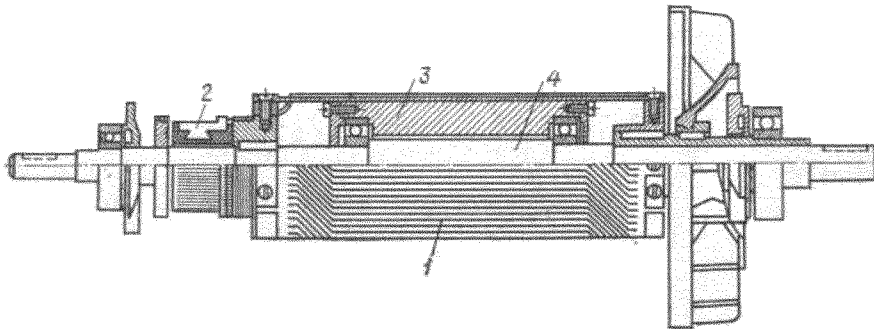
Цилиндрический якорь с печатной обмоткой (в сборе)
